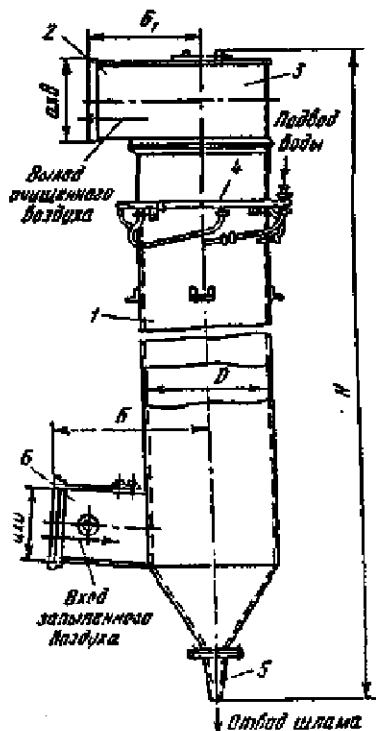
Циклон с водяной пленкой ЦВП: 1 - корпус; 2 - выходной патрубок; 3 - улитка; 4 - коллектор; 5 - конусный патрубок (гидрозатвор); 6 - входной патрубок.
